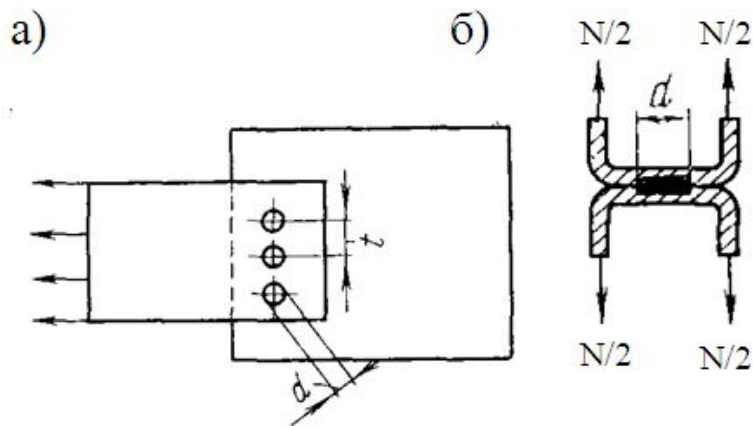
Схемы точечных сварных соединений:
